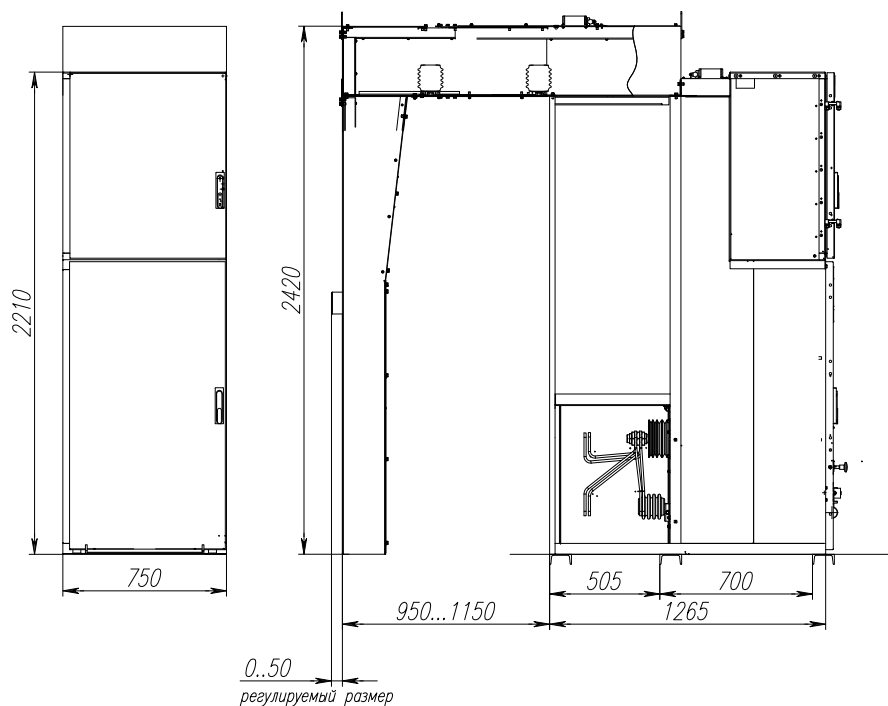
Общий вид и габаритные размеры шкафа К-128 кабельного ввода на номинальные токи до 1600 А (ввод через блок)
